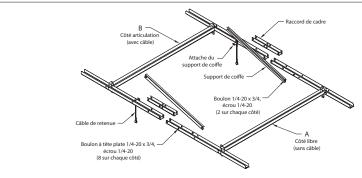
Assemblage du cadre de coiffe 3FKE2 et 3FKE3
